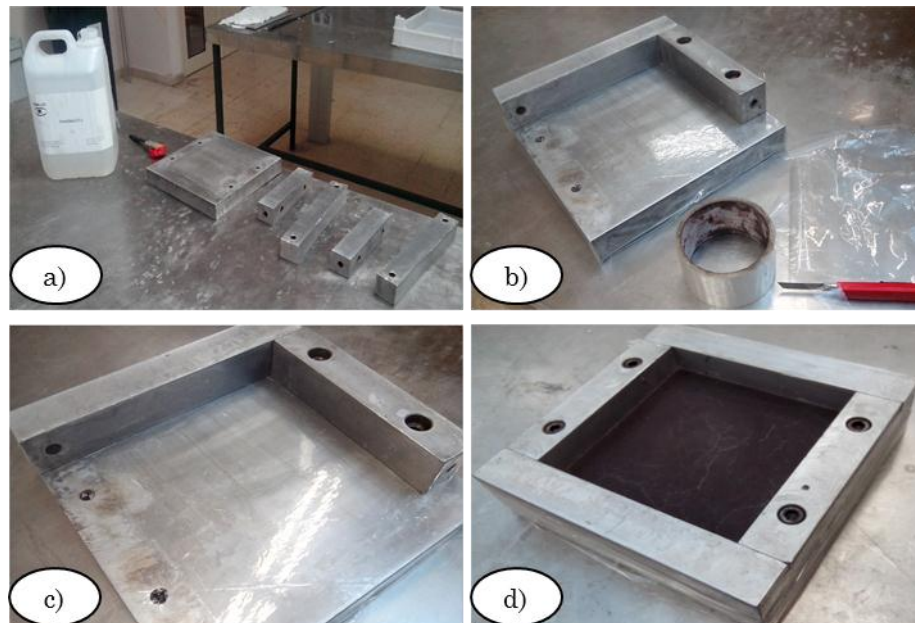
Molde metálico para o processamento de placas. a) Aplicação de desmoldante; b) Aplicação de película antiaderente e fita-cola; c) Montagem do molde; d) Molde com placa em processo de cura.
